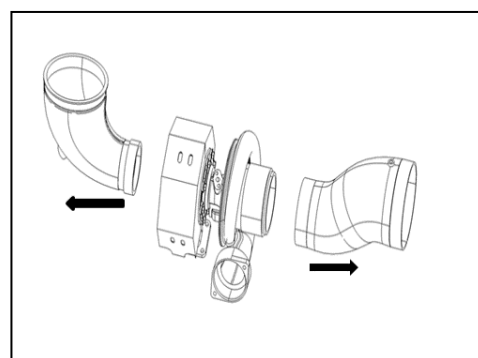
Ж Патрубки турбокомпрессора
